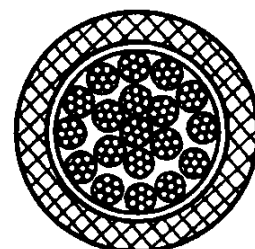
Схема одножильного кабеля КОГ2 для дуговой электросварки
